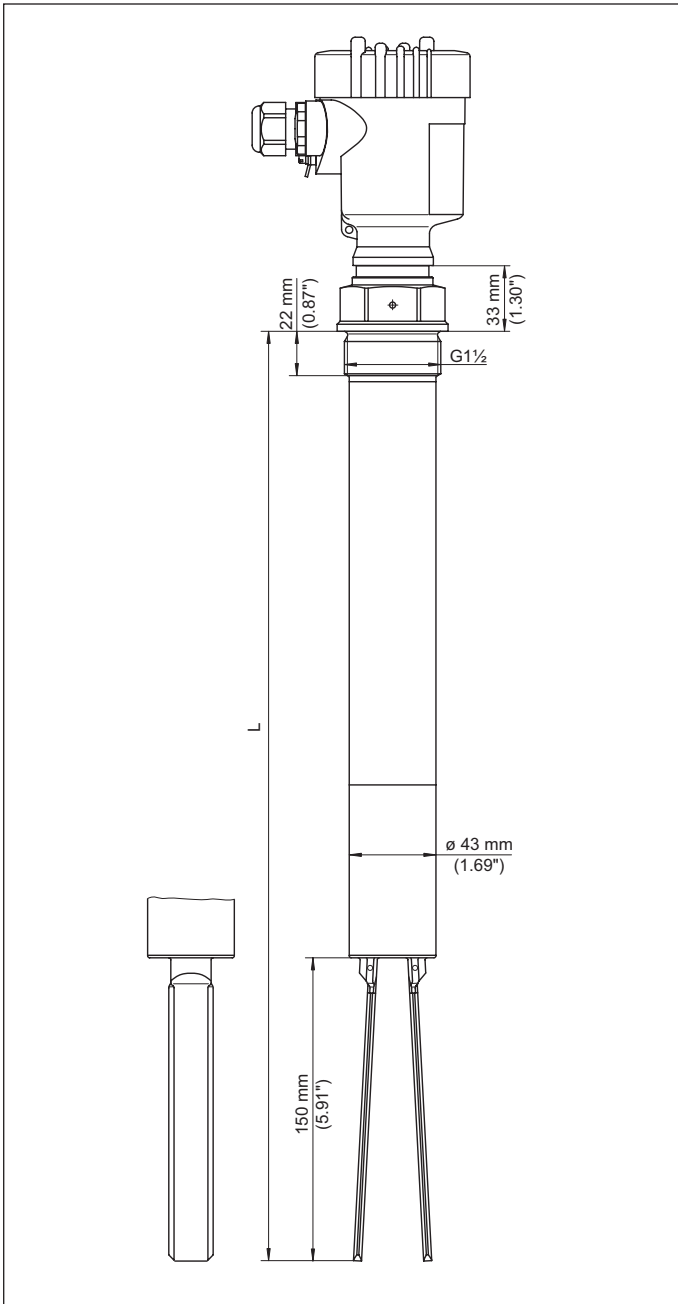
VEGAWAVE 63 - Gewindeausführung G1½
